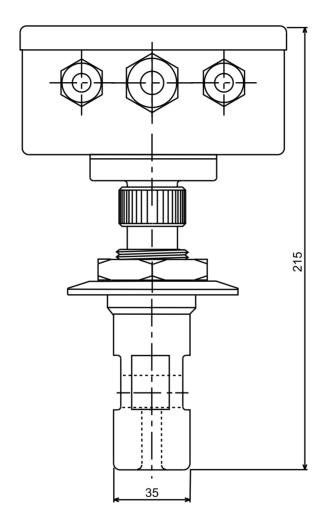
Габаритные размеры датчика IET40L с хомутным присоединением (вид спереди)
